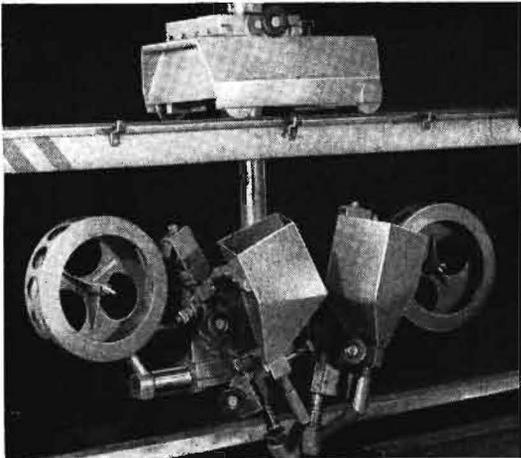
UP-Tandemschweißautomat ZIS 386
